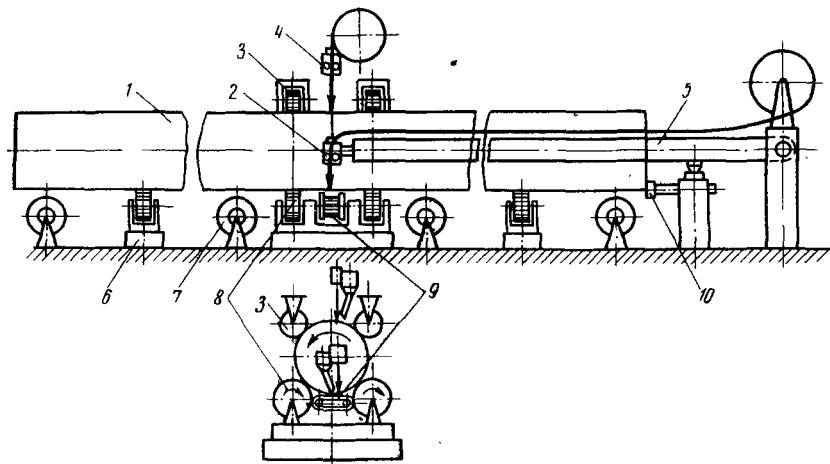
Схема установки для двусторонней сварки стыков труб
